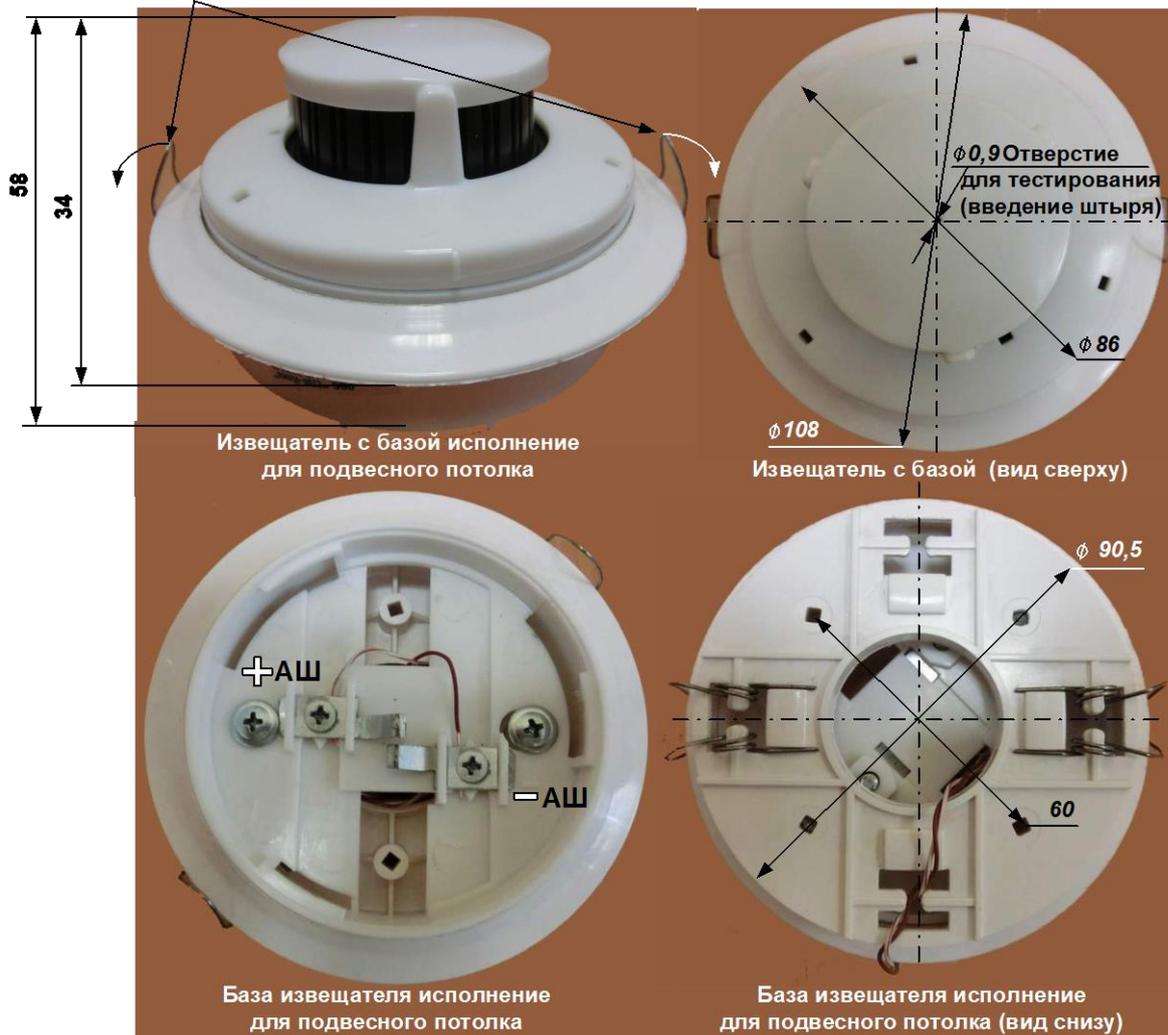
АЗДПИ с базой. Габаритные и присоединительные размеры
